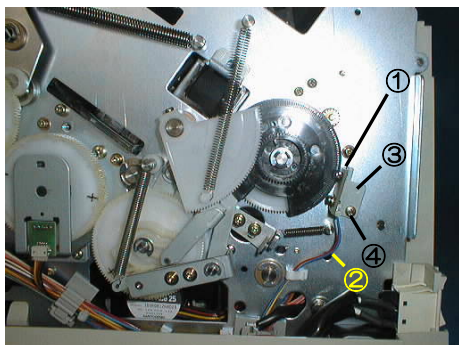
Gap Sensor Board、Cable Sensor Head Gap (その 1)
